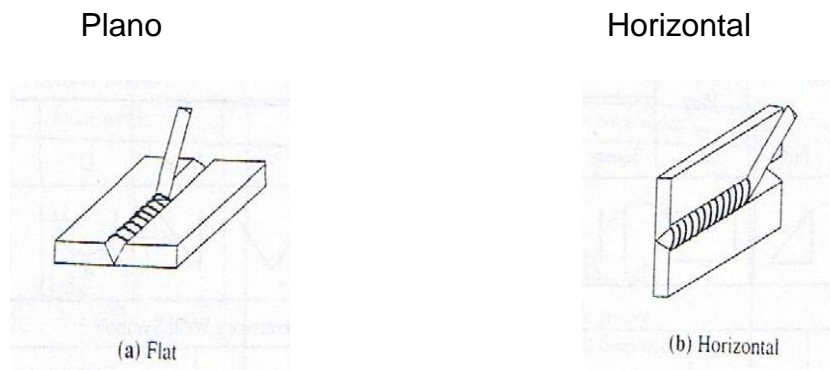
Posiciones de soldadura del S.A.S.<sup>4</sup>
